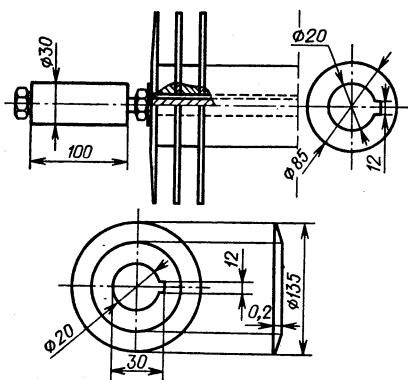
Скалка с дисковыми ножами для ручной резки корпусов конфет «Грильяж в шоколаде»
